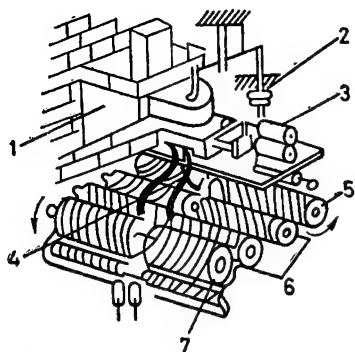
Instalație de fabricat bile de sticlă (vedere parțială):
